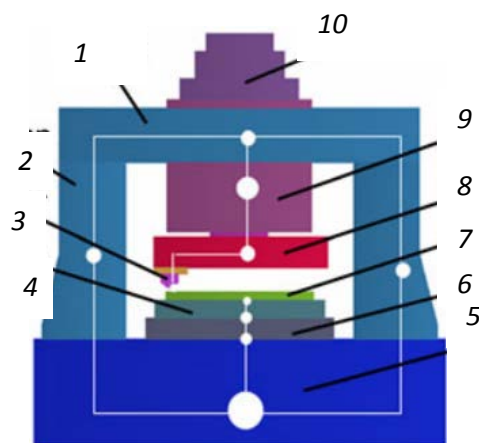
Компоновочное решение станка микрофрезерования [5]:
